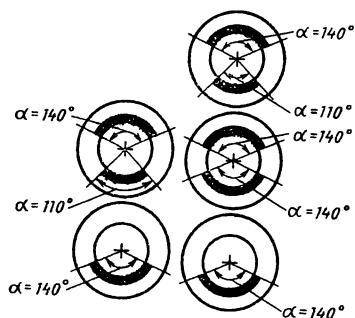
Расположение вкладышей в подшипниках открытого типа
